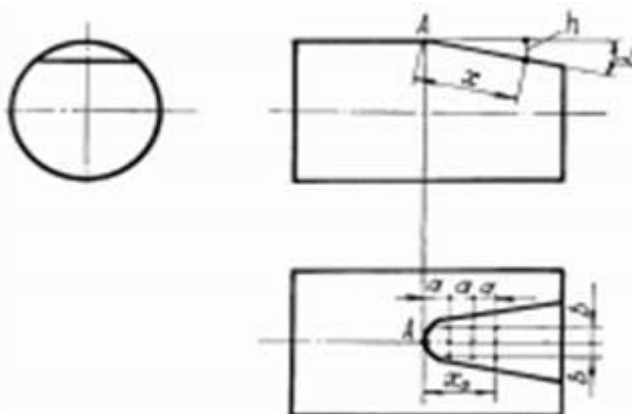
Креслення цилін-дричного зразка з косим зрізом і схема вимірювання твердості поверхні.
